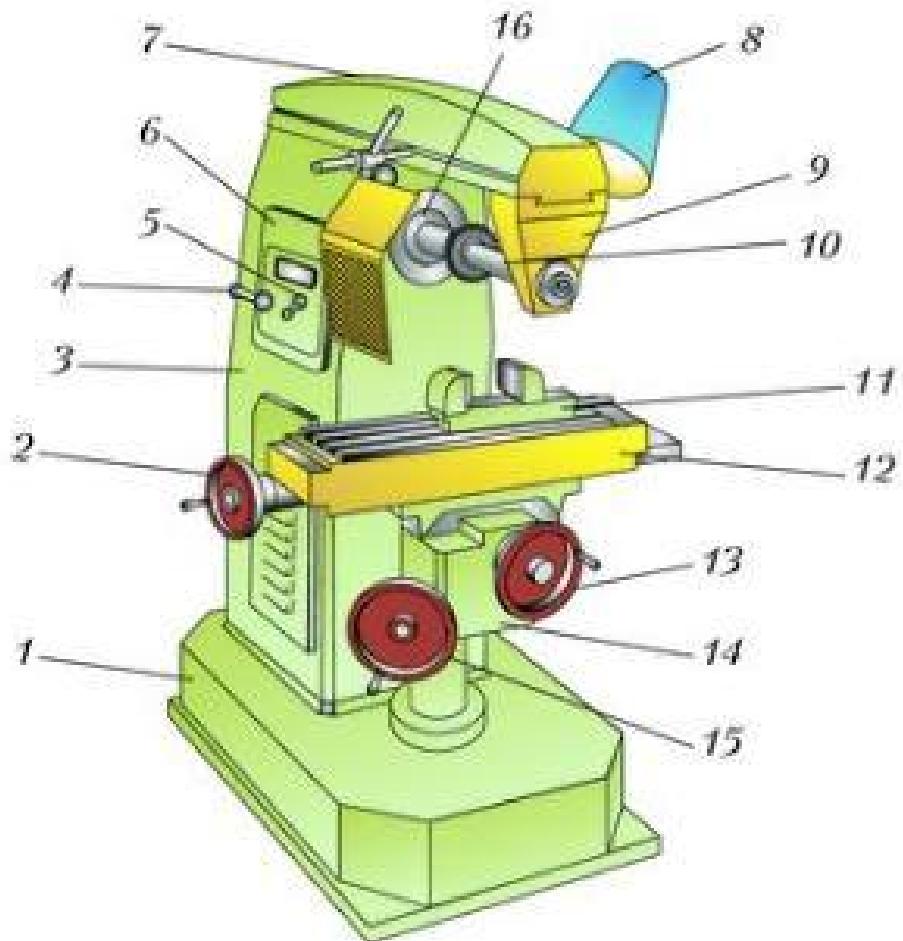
Устройство горизонтально-фрезерного станка НГФ-110Ш: 1 – основание; 2 – маховик продольной подачи; 3 – корпус станка; 4, 5 – рукоятки переключения частоты вращения шпинделя; 6 – коробка скоростей; 7 – хобот; 8 – светильник; 9 – серьга; 10 – оправка с фрезой; 11 – тиски; 12 – стол; 13 – маховик поперечной подачи; 14 – консоль; 15 – маховик вертикальной подачи; 16 – шпиндель
